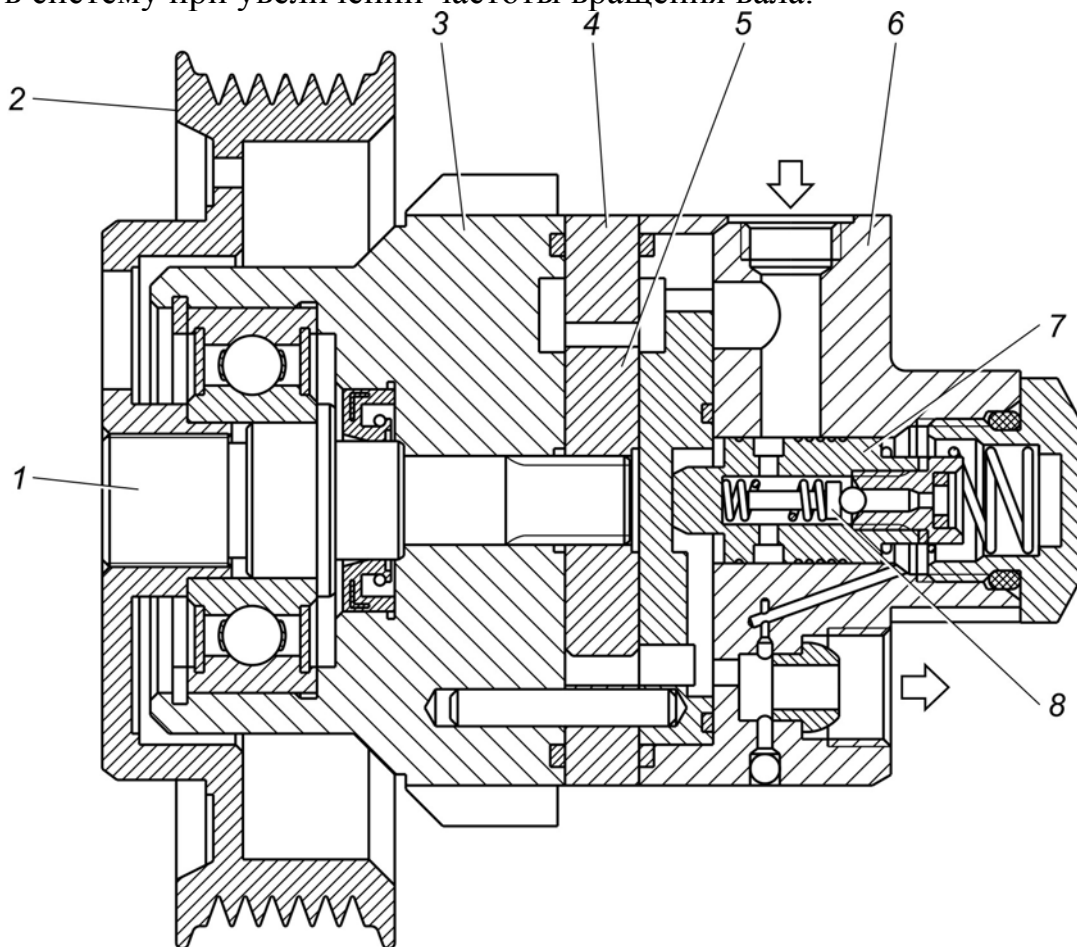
Насос гидроусилителя: 1 - вал; 2 - шкив; 3 - корпус; 4 - статор; 5 - ротор; 6 - крышка; 7 - клапан расхода; 8 - предохранительный клапан
